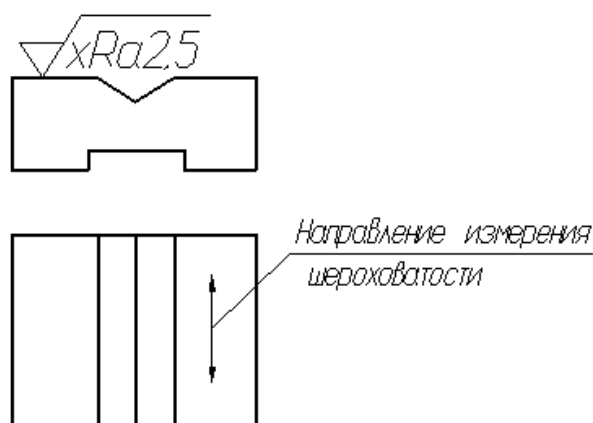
Пример указания направления измерения шероховатости поверхности.
